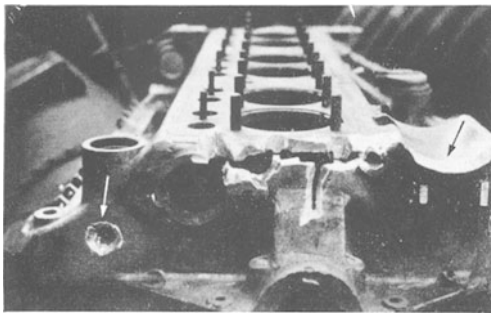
Elektrongehäuse eines Sechszylindermotors für die Schweißung vorbereitet.
